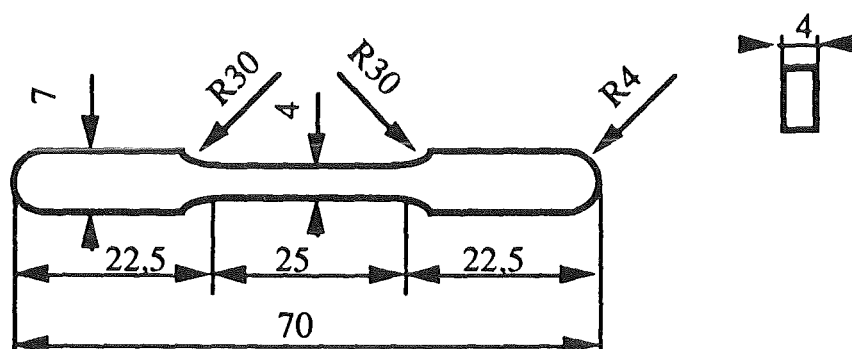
Geometrie des Zugstab-Preßwerkzeuges [73].
